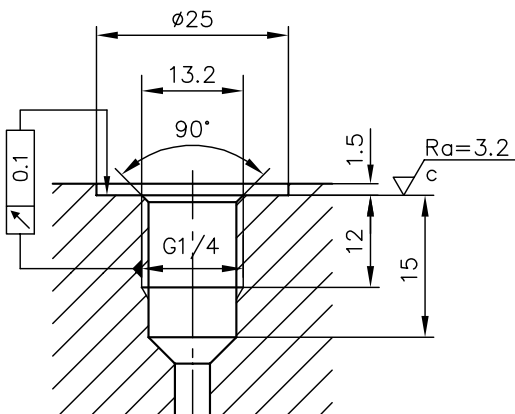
Резьба для ввинчивания DIN 3852-X-G 1/4
